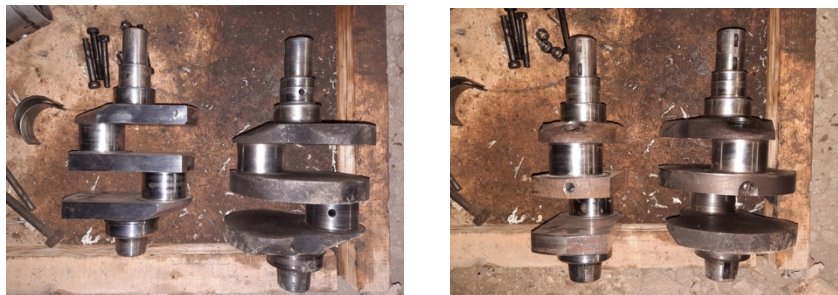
Внешний вид доработанного и стандартного коленчатых валов под разными углами
